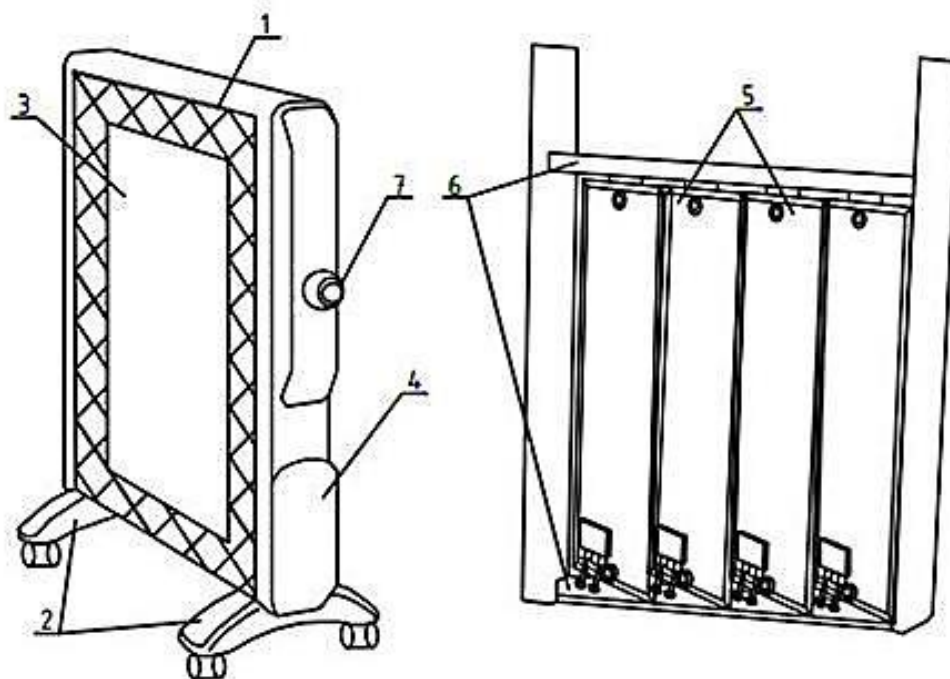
Общий вид инфракрасного обогревателя и нагревательного элемента
